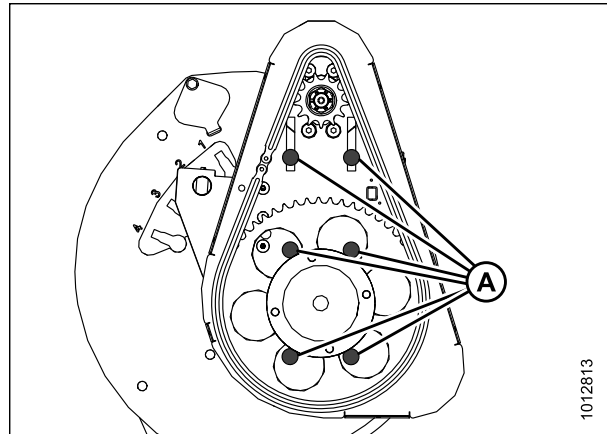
Изображен привод единого мотвила — привод сдвоенного мотвила имеет такую же конструкцию
